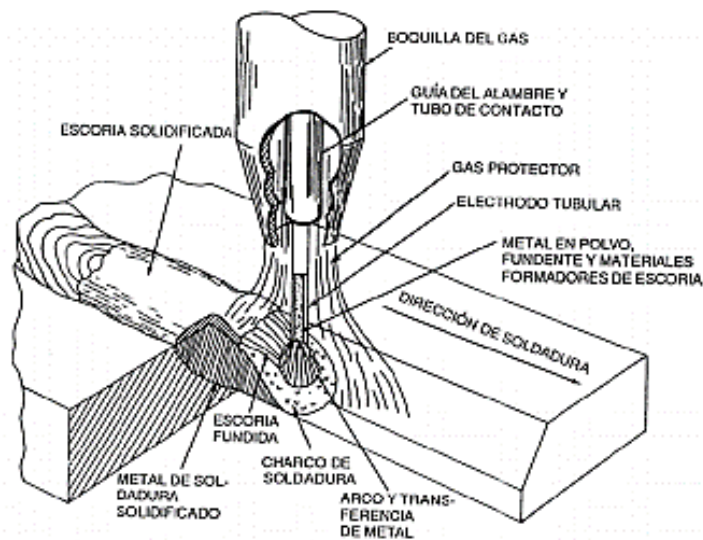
Soldadura por Arco con Núcleo de Fundente protegida con Gas [10].
